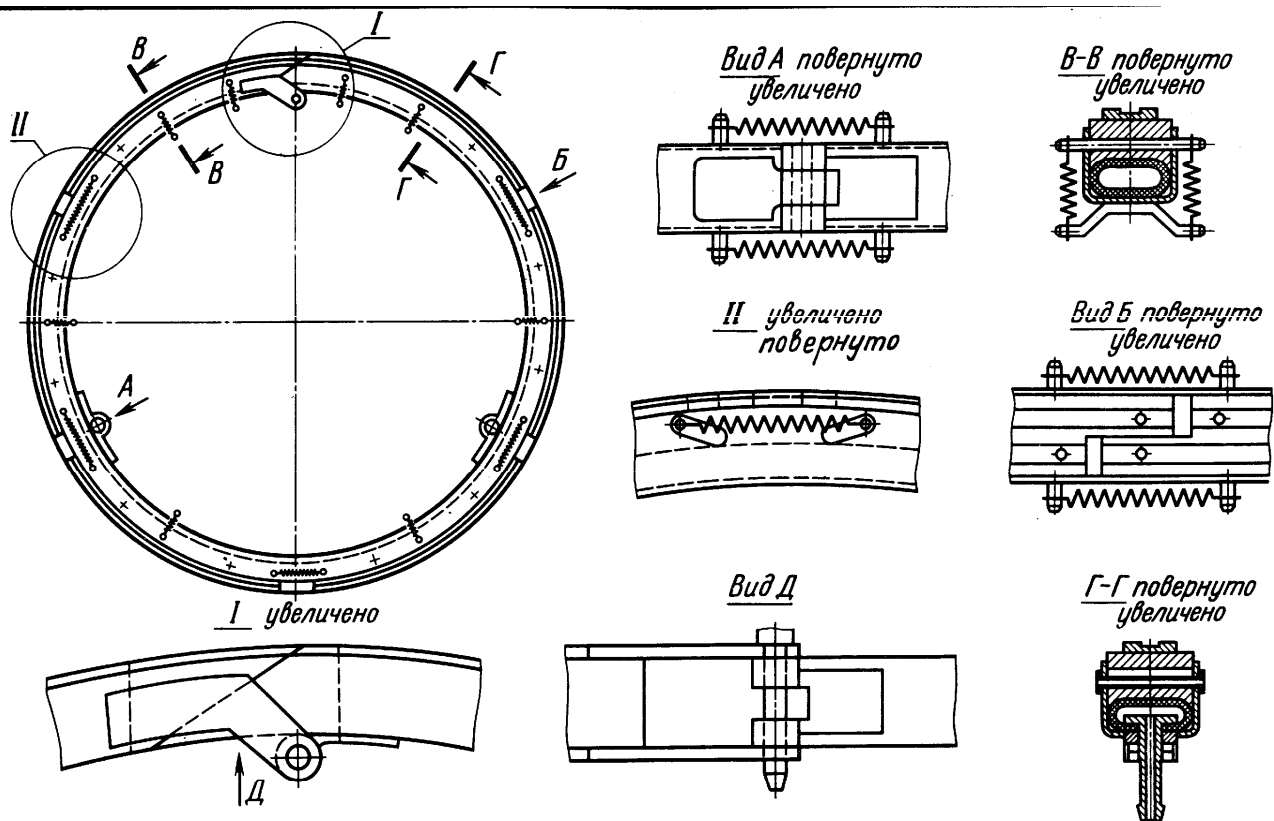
Распорное кольцо пневмошлангового типа для сварки кольцевых швов
